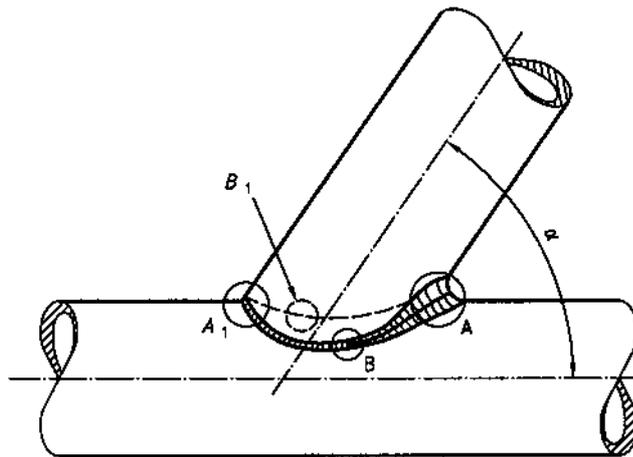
Расположение образцов для испытаний отвода углового сварного шва при сварке труб
